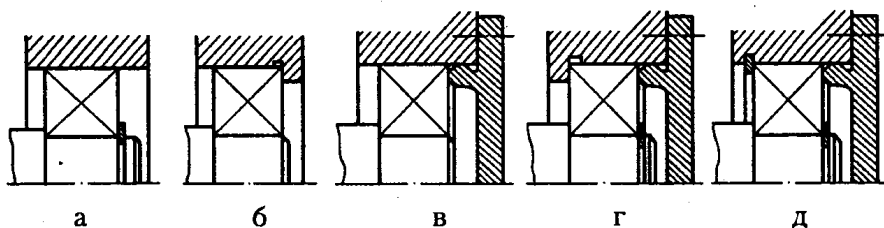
Кріплення підшипників кочення у корпусі опори
